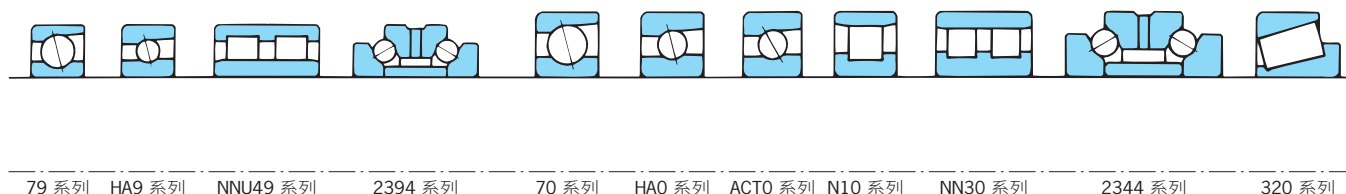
机床用精密滚动轴承的形式和各尺寸系列的轴承安装空间
